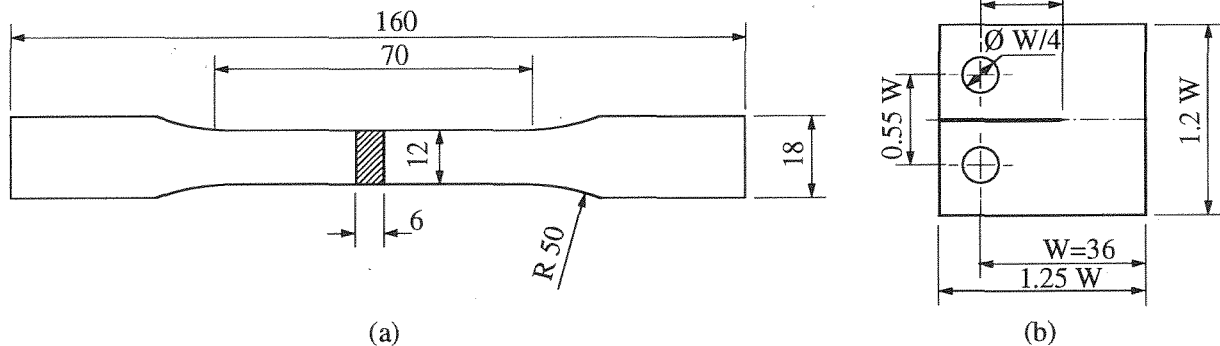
Geometria dos provetes (dimensões em mm): a) ensaios de tracção; b) ensaios de tenacidade à fractura
